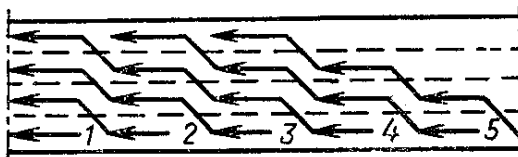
Схема сварки длинных многослойных швов каскадом.
